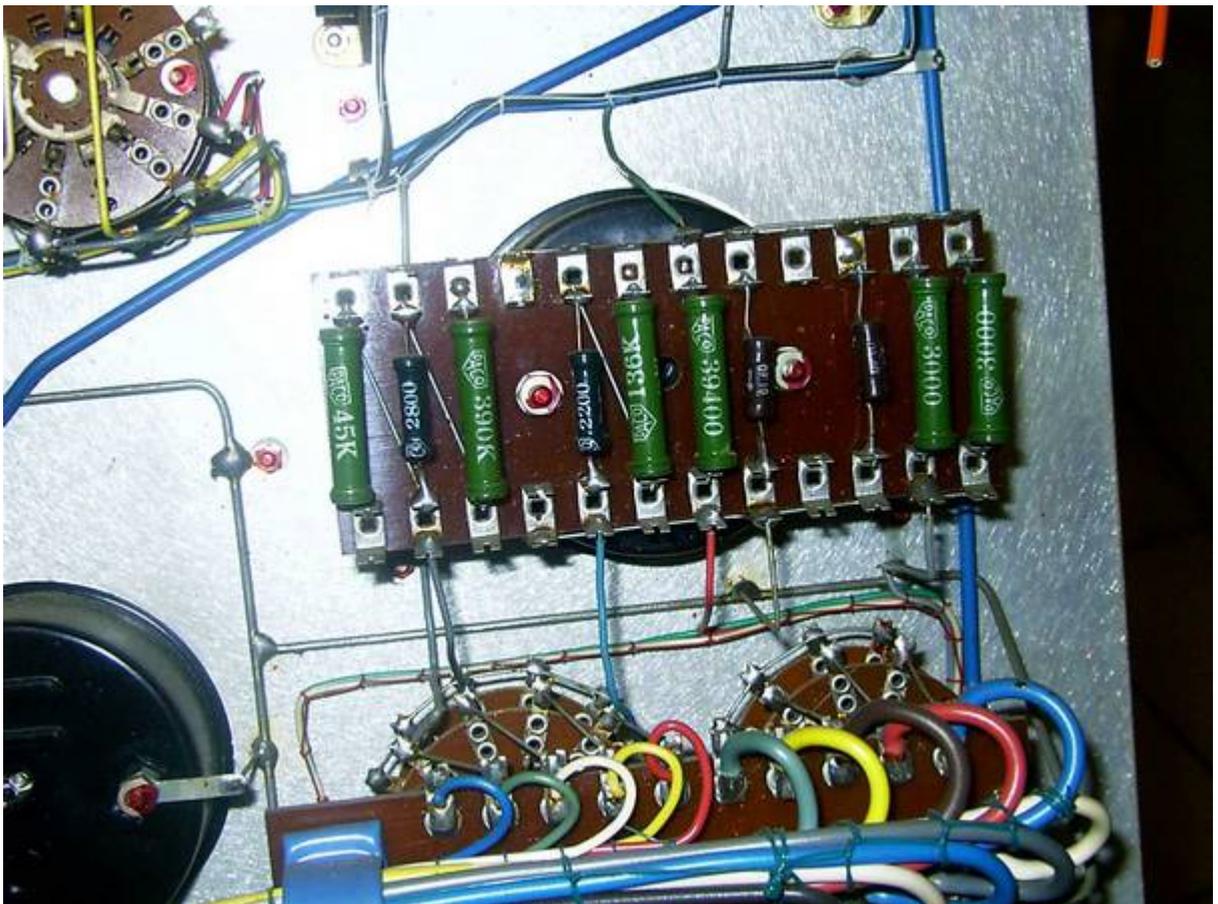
platine initiale galvanomètre tension filament d'un U61.
